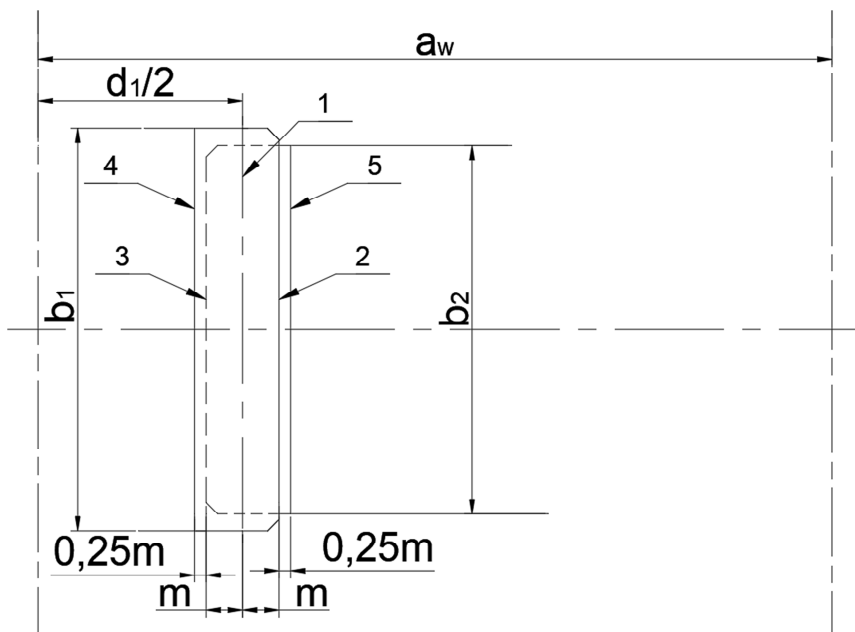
Зацепление цилиндрических зубчатых колес
